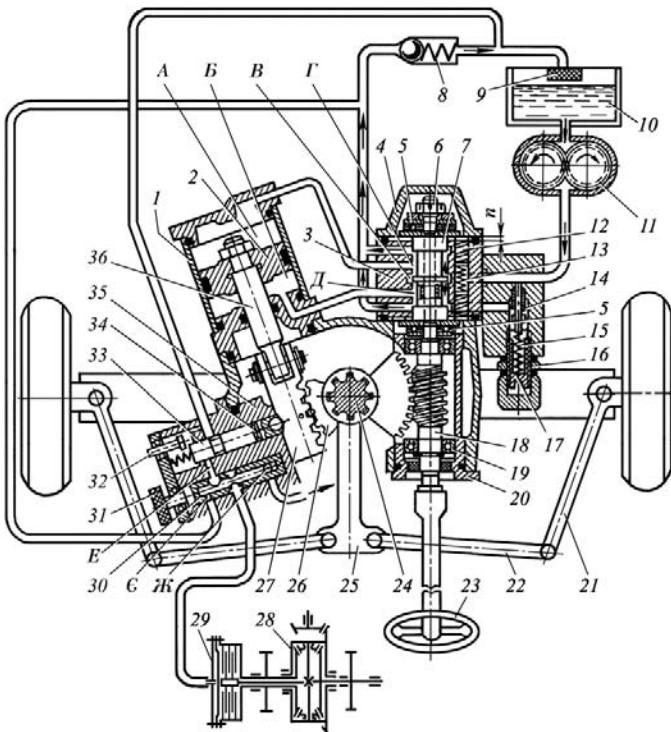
Схема рулевого управления с гидроусилителем трактора МТЗ-80: 1 — силовой цилиндр; 2 — поршень; 3 — корпус распределителя; 4 — крышка; 5 — упорный по дшипник; 6 — гайка; 7, 33 — золотники; 8 — редукционный клапан; 9 — фильтр; 10 — масляный бак; 11 — шестеречатый насос; 12 — ползун; 13 — центрирующая пружина; 14 — предохранительный лынчевый клапан; 15 — пружина; 16 — контргайка; 17 — регулировочный винт; 18 — червяк; 19 — шариковый подшипник; 20 — эксцентричная втулка; 21 — поворотный рычаг; 22 — рулевая тяга; 23 — рулевое колесо; 24 — поворотный вал; 25 — сошка; 26 — сектор; 27 — рейка; 28 — дифференциал; 30 — кран; 31 — маховичок; 32 — щуп; 34 — толкатель; 35 — упор; 36 — шток силового цилиндра; А, Б — полости силового цилиндра; В — средняя нагнетающая виточка; Г, Д — крайние сливные выточки; Е — сливной канал датчика; Ж — дроссельное отверстие.
